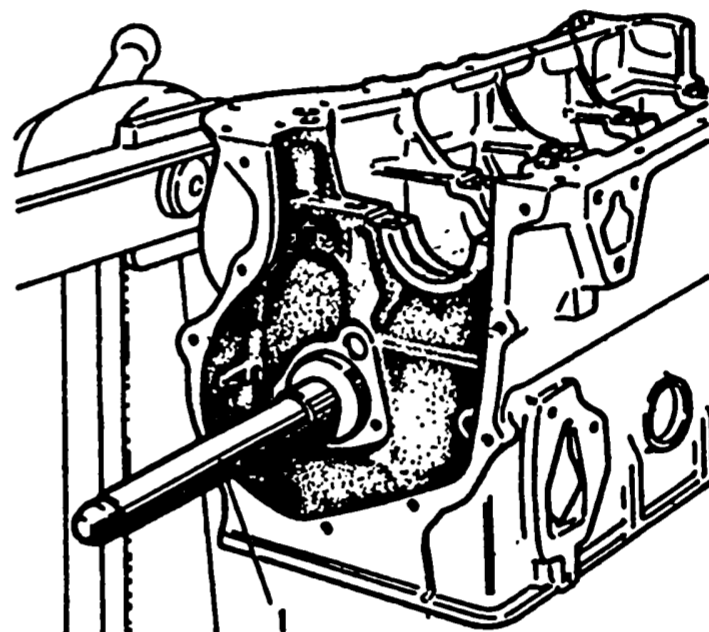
Снятие и установка втулок валика привода масляного насоса: 1 - оправка А.60333/1/2
